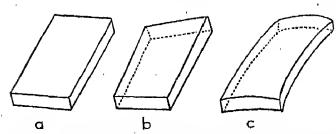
Les planches, débitées à la scierie dans les grumes, ne restent pas planes; elles gauchissent plus ou moins, à la langue, en séchant: a) planche légèrement tordue; b) planche fortement tordue; c) planche bombée.
